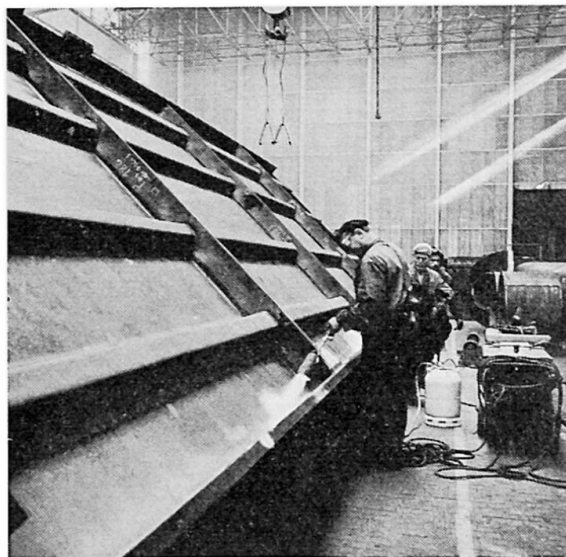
Préchauffage des semelles avant soudure.
